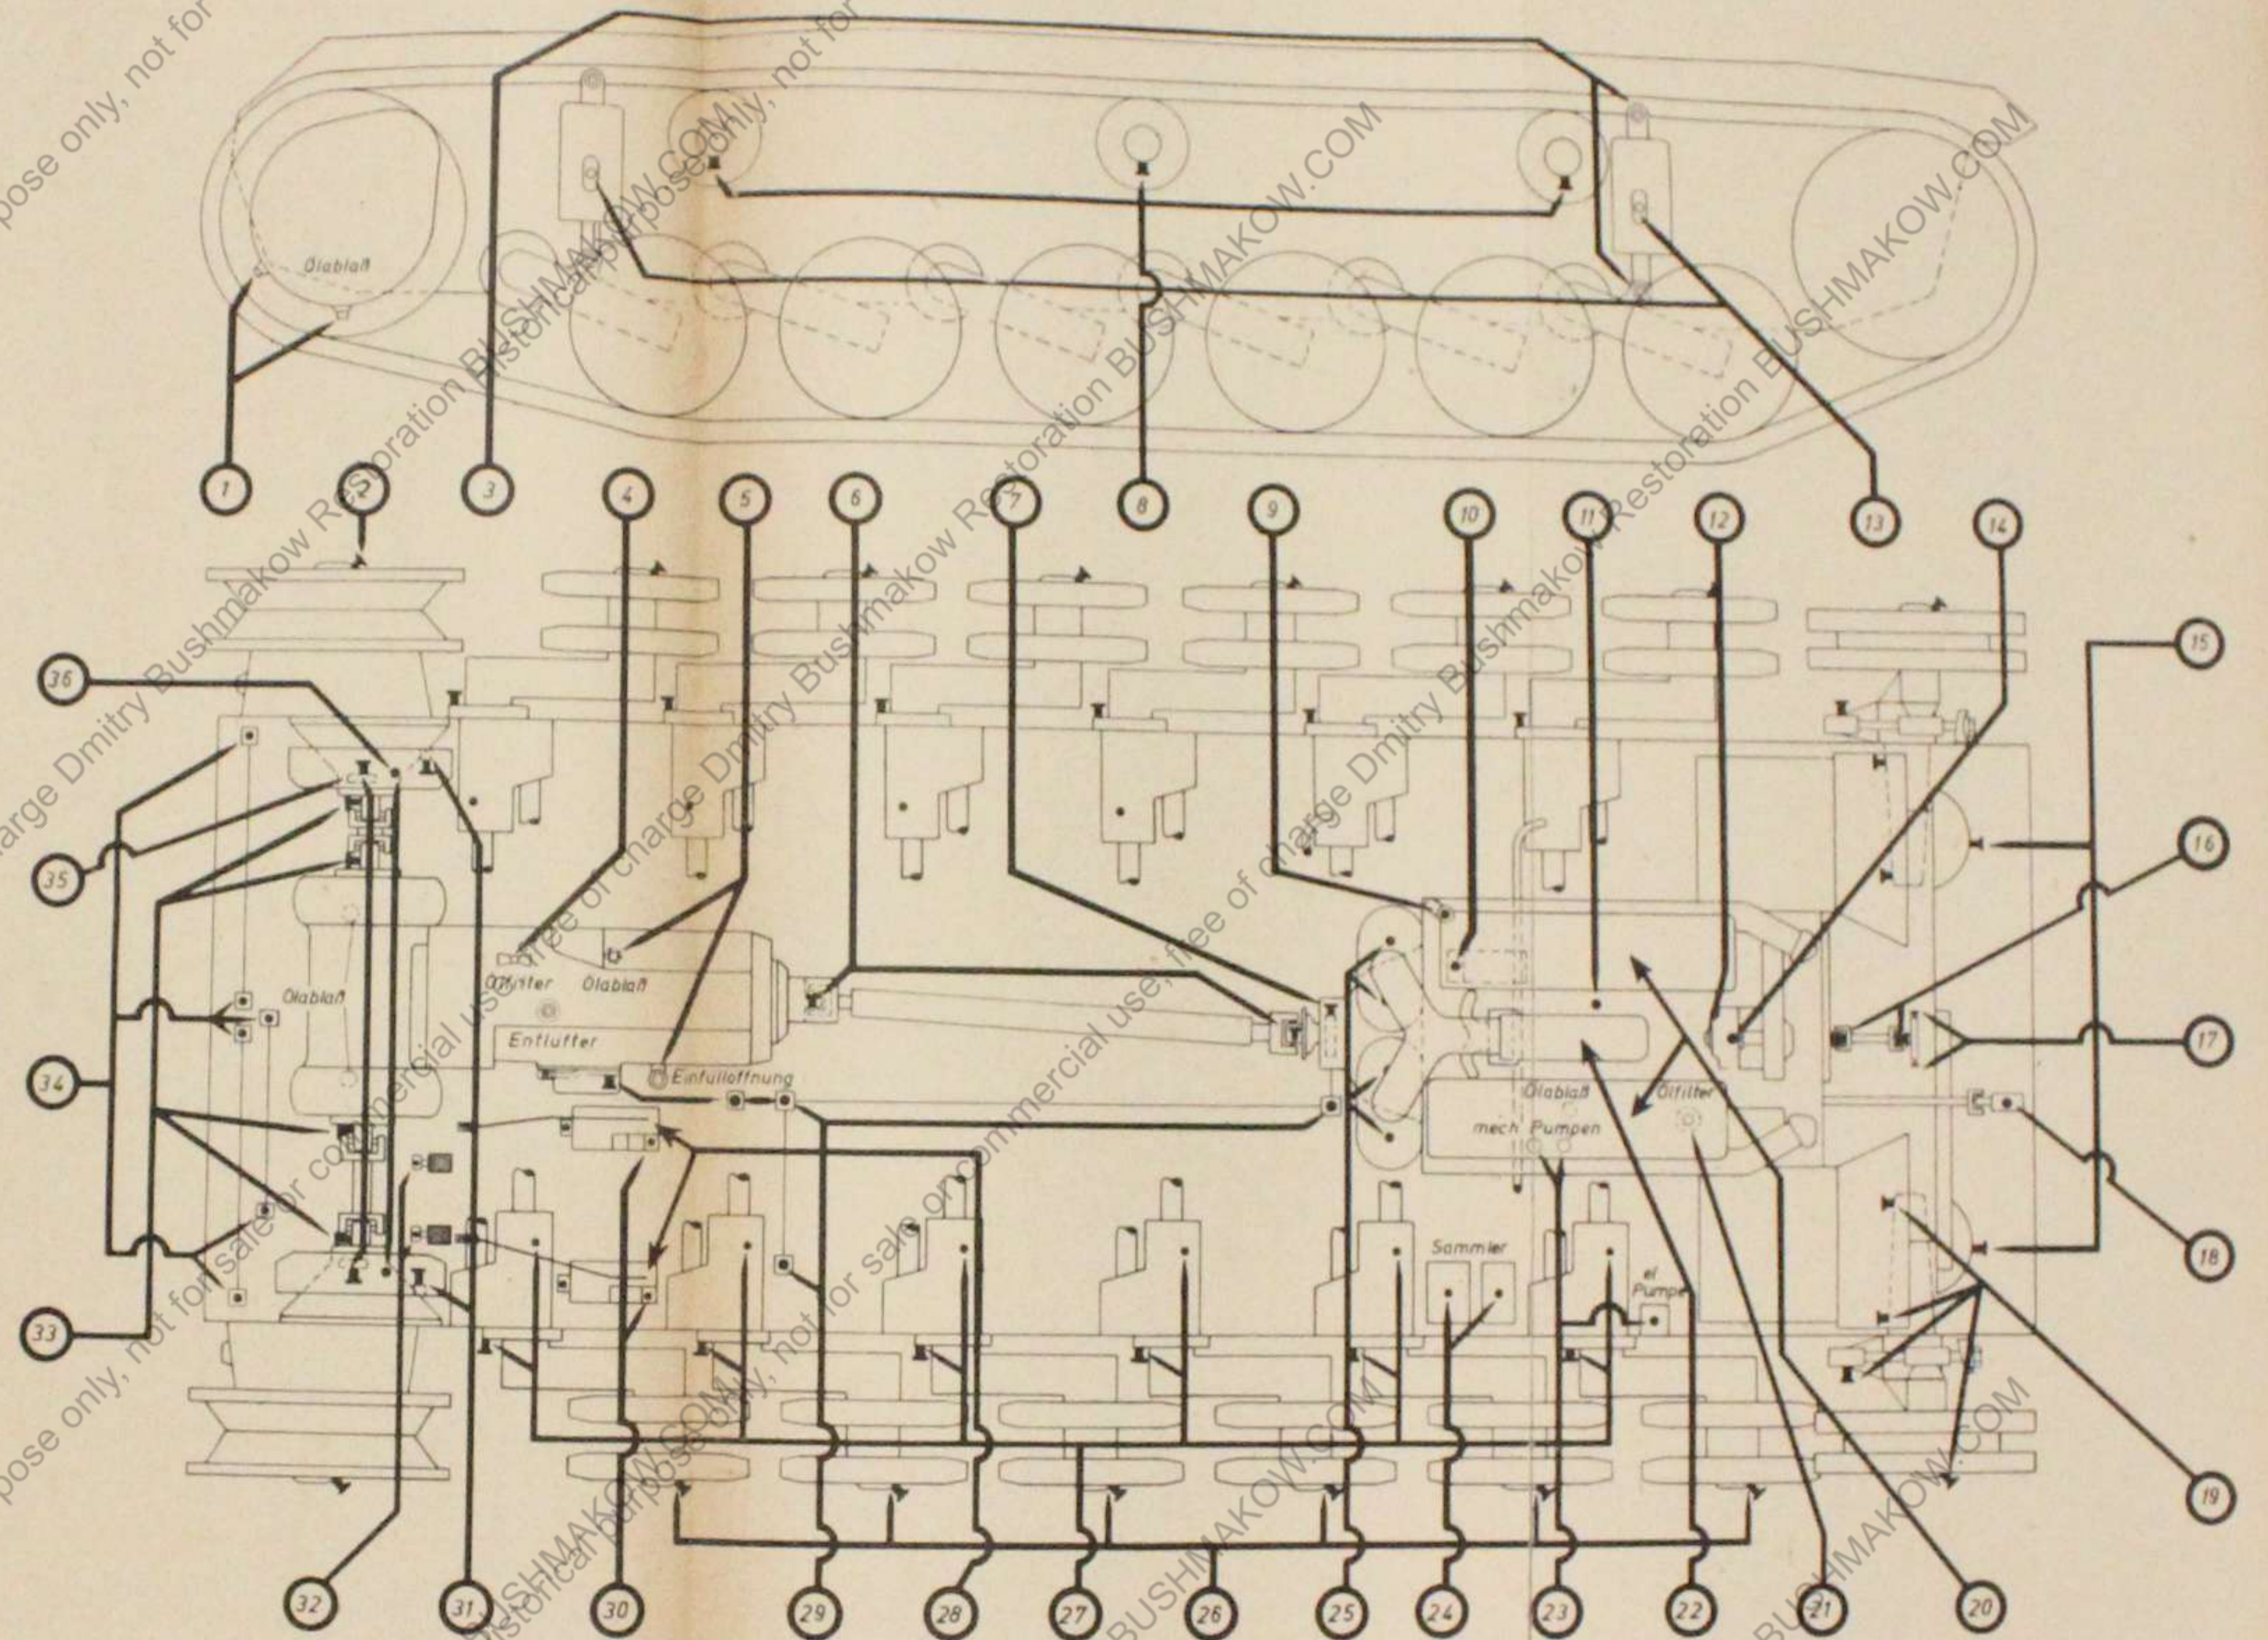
a Schmier- und Pflegeplan, Ausj. B-F
